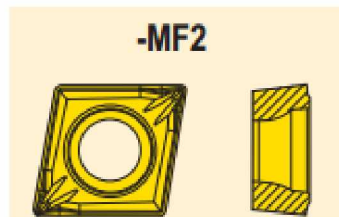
Ромбічна пластина для чистової обробки CCMT060204 -MF2
